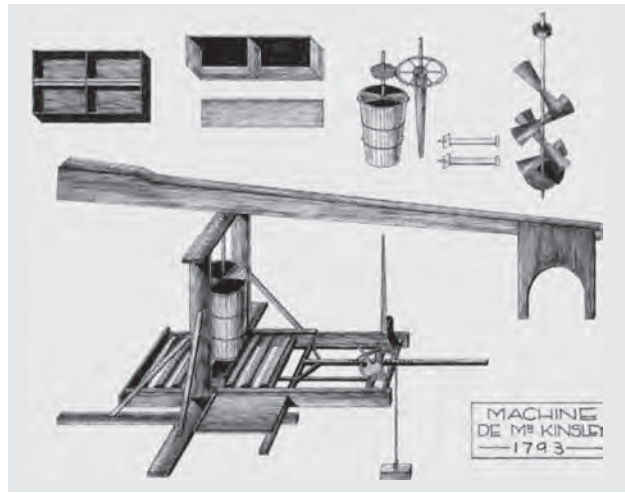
Ziegelmaschine von Kinsley, 1793
